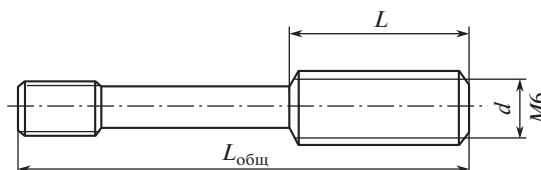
Резьбовой калибр, формирующий резьбу:  $L_{\text{общ}}$  — общая длина калибра;  $L$  — длина рабочей части калибра;  $d$  — внутренний диаметр резьбы.
